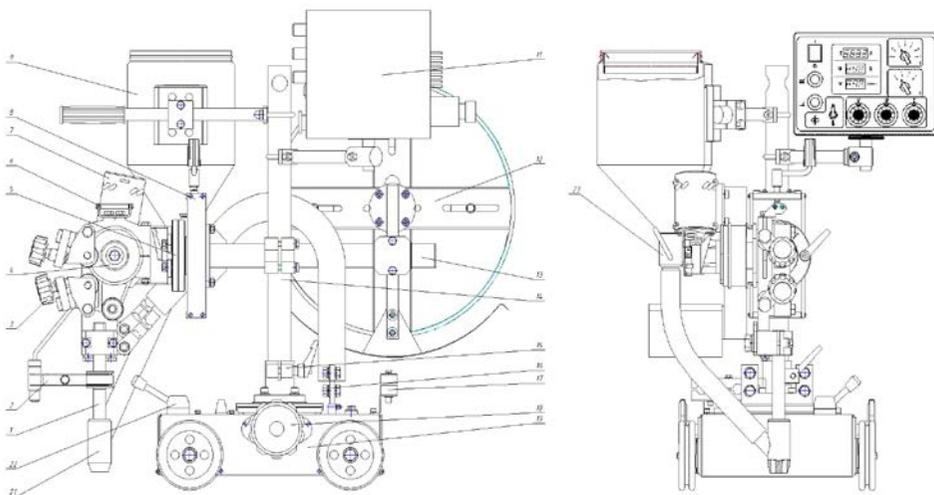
Общий вид трактора сварочного АДФ-1000
